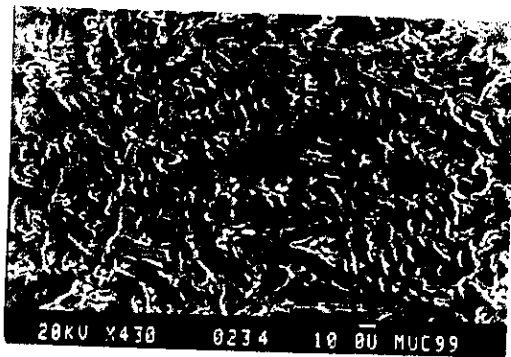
Baño fundido, zona central del cordón de soldadura.
